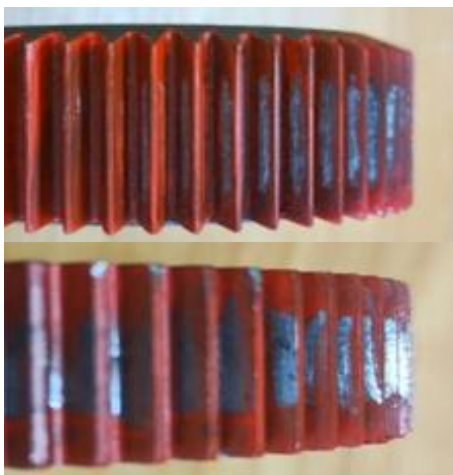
Мгновенное пятно контакта при обкатке инструмента и заготовки
